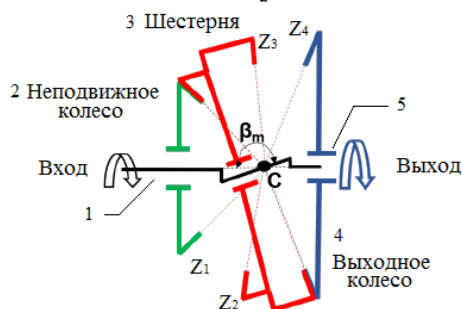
Принципиальная схема волнового торцевого кинематического редуктора
